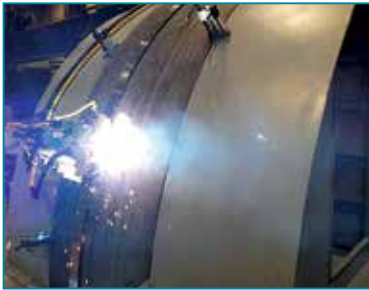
Лазерно-дуговой мобильный сварочный комплекс «Орбита»
